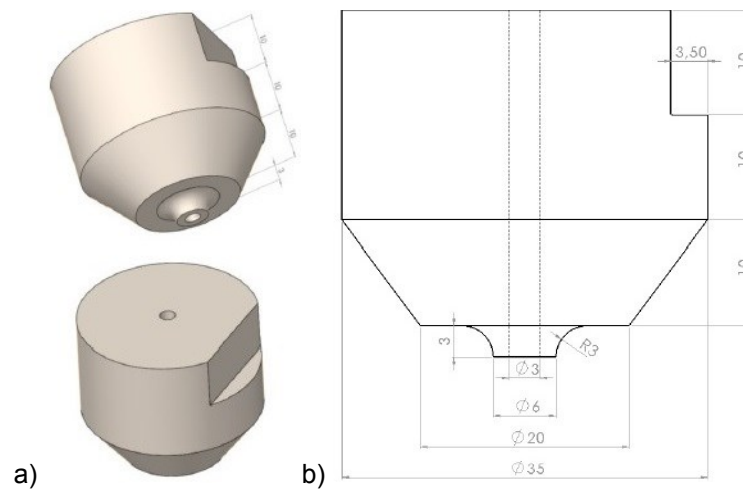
Ferramenta em alumina; a) Perspetiva, b) Desenho Técnico.
